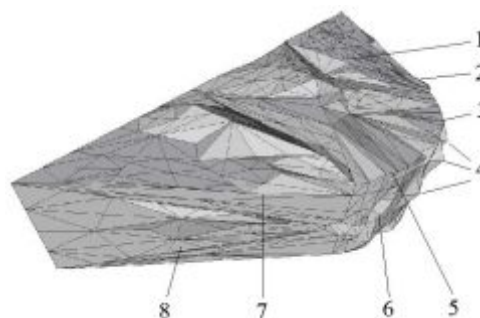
Результат трехмерной реконструкции 3D-модели режущей части резца для прецизионной обработки, выполненной по базовому алгоритму: 1 – образ передней поверхности; 2 – образ главной режущей кромки; 3 – образ переходной режущей кромки; 4 – артефакты модели в области переходной задней поверхности РЧ; 5 – артефакты модели в области передней поверхности РЧ; 6 – образ переходной задней поверхности РЧ; 7 – образ вспомогательной режущей кромки РЧ; 8 – образ вспомогательной задней поверхности РЧ
